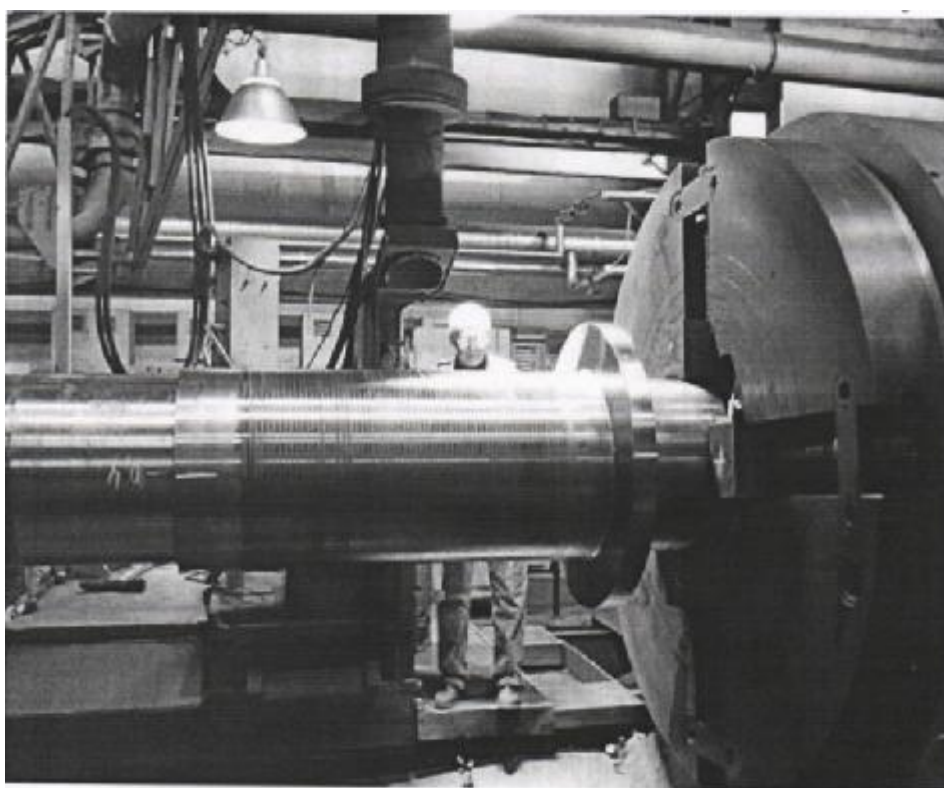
Закалка шейки шпинделя тяжелого токарного станка
